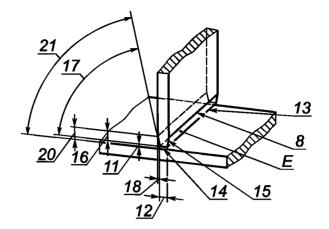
Подготовка под сварку таврового соединения с двусторонним скосом кромки
